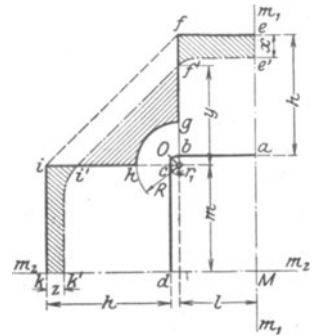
Zuschnittsberechnung für Hohlgefäße mit rechteckigem Boden (rechteckiger Hohlgefäße).
